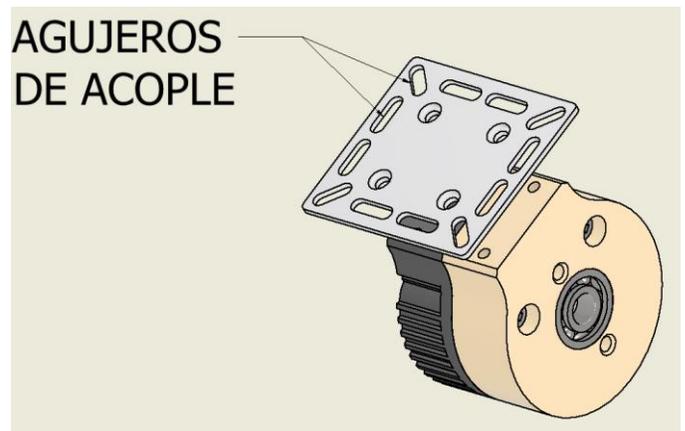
Modelado de acople para herramientas, Fuente: Autor
